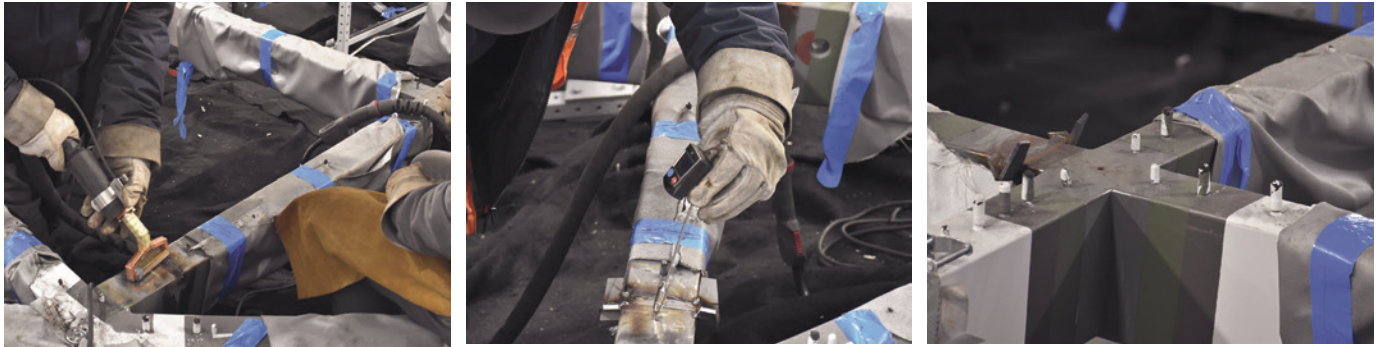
Links: Vorwärmen mit dem Induktor von Hand; Mitte: Messung der Vorwärmtemperatur; rechts: fertige Schweißnaht vor dem Entfernen der Ein-/Auslaufbleche (© VauQuadrat GmbH)
